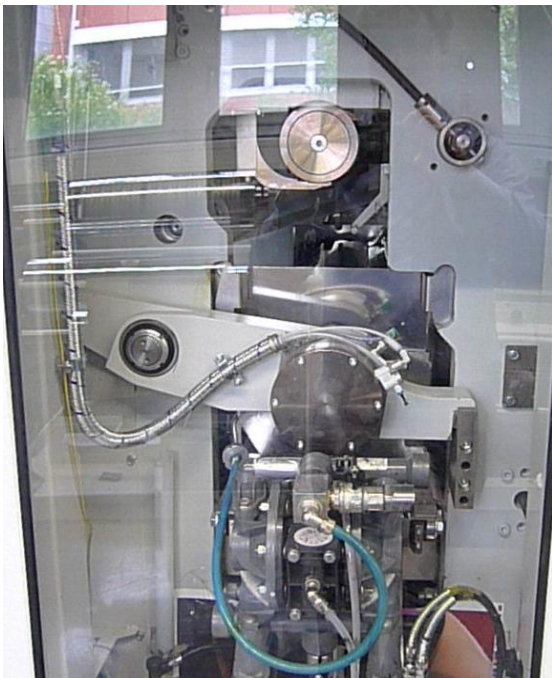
Zylinderrevolver zur Maschinenbestückung
